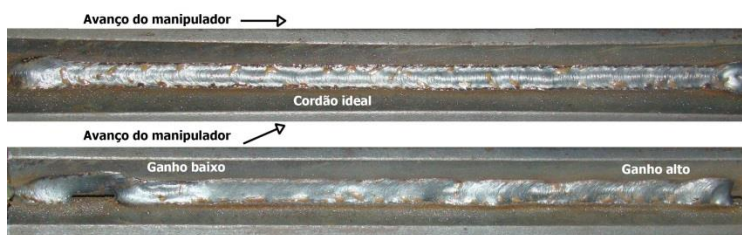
Exemplo da presença de erro em regime permanente em soldagem com seguimento automático de junta (soldagem alinhada acima e soldagem desalinhada abaixo).
